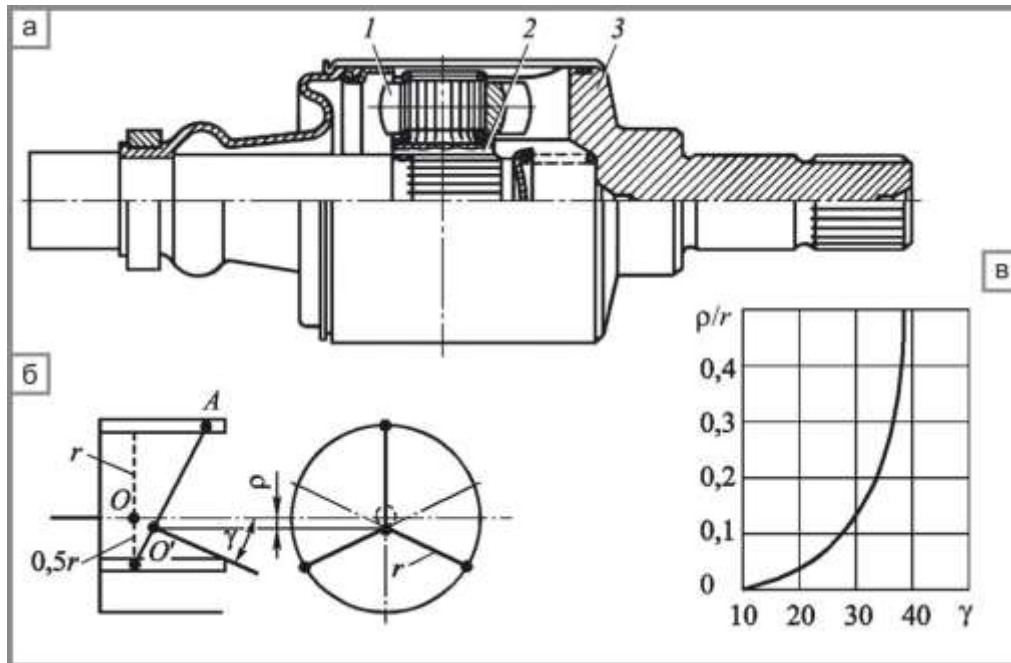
Конструкція (а), схема (б) та характеристики (в) тришипового карданного шарніра (типу «Трипод»): 1 — ролики; 2 — маточина; 3 — корпус
